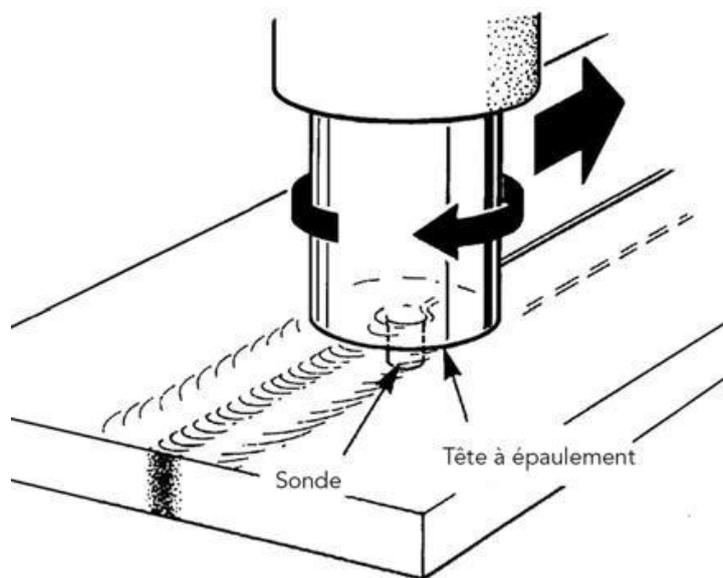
a : Soudage par friction-malaxage [3].
